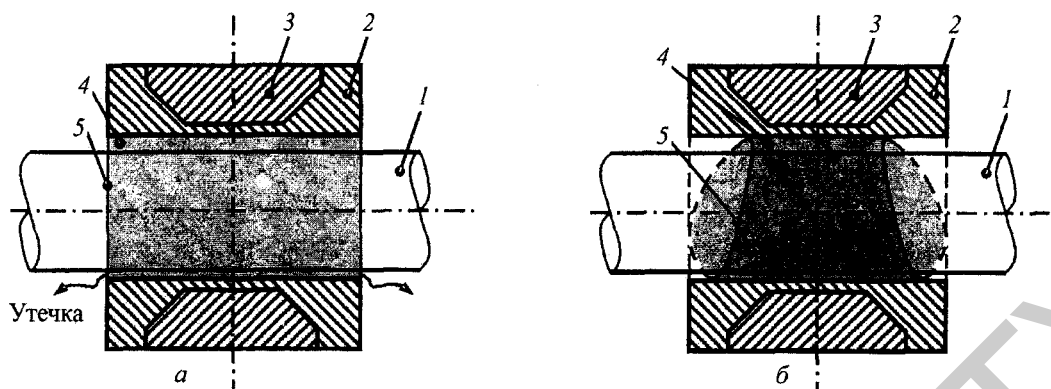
Схематичное изображение магнитожидкостного подшипника с фиксированной границей смазочного слоя (а) и со свободной границей (б): 1 — вал; 2 — немагнитная обечайка подшипника; 3 — постоянный магнит; 4 — магнитная жидкость; 5 — боковые границы смазочного слоя (передняя — а и задняя — б)
